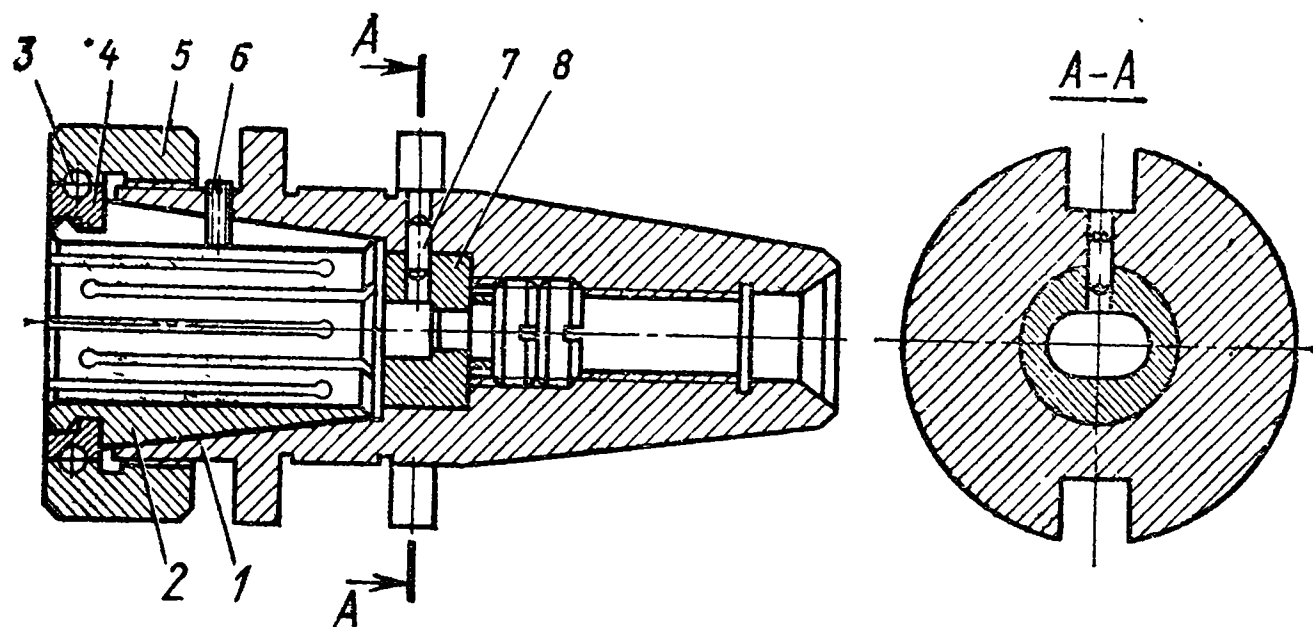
Цанговый патрон для крепления инструментов с цилиндрическим хвостовиком
